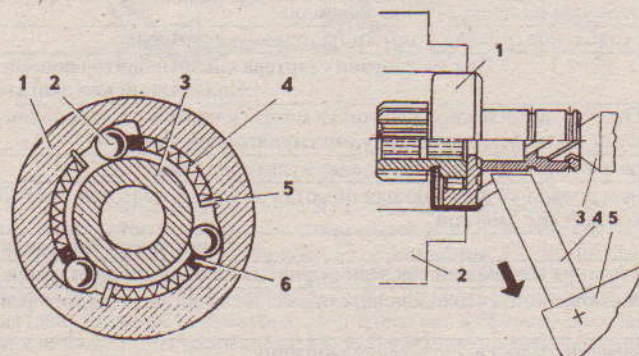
Развальцовка крышки привода на токарном станке: 1 - привод; 2 - патрон станка; 3 - задний центр; 4 - инструмент; 5 - резцедержатель
